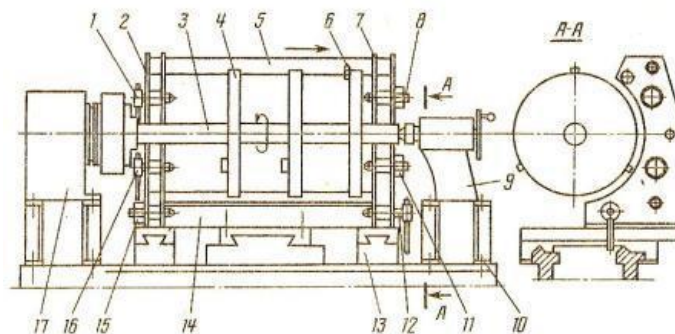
Приспособление для растачивания планок подбарабанья на токарно-винторезном станке: 2 – Левый кронштейн; 7 – Правый кронштейн; 9 – Задняя бабка; 13 – Дополнительный суппорт; 17 – Передняя бабка.
